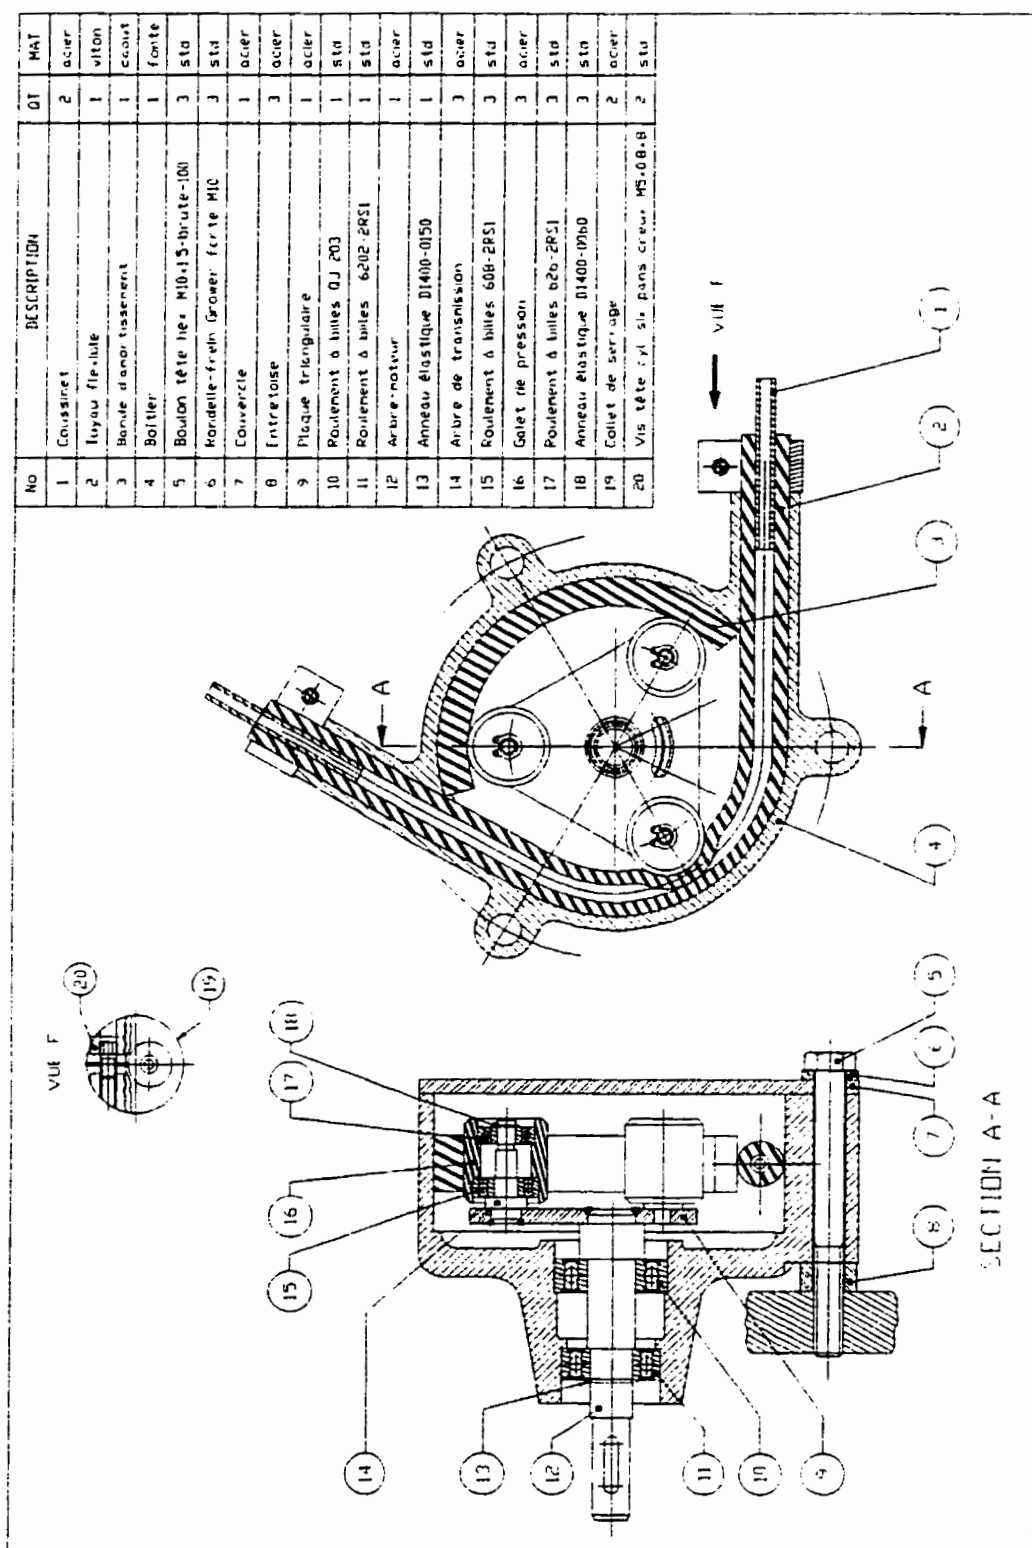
Dessin d'ensemble d'une pompe à corps déformable
